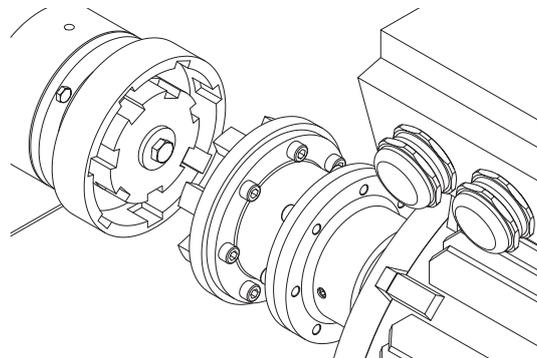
Pumpen- u. motorseitige Kupplungshälfte
